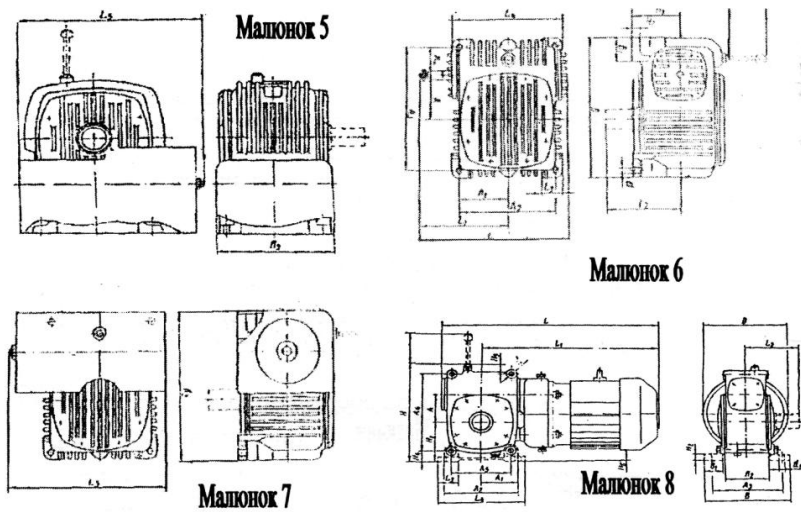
Редуктор РГНВ. Рис. 7. Редуктор РГБ. Рис. 8. Редуктор РГНВ. Рис. 9. Мотор-редуктор МРГУ.
